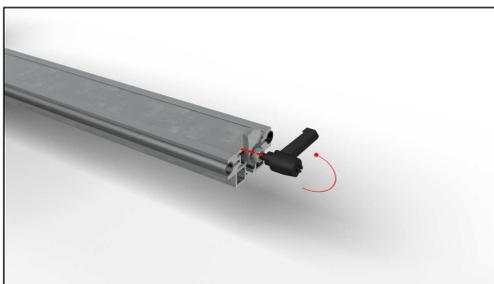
Ruotare vite di assemblaggio guide.
